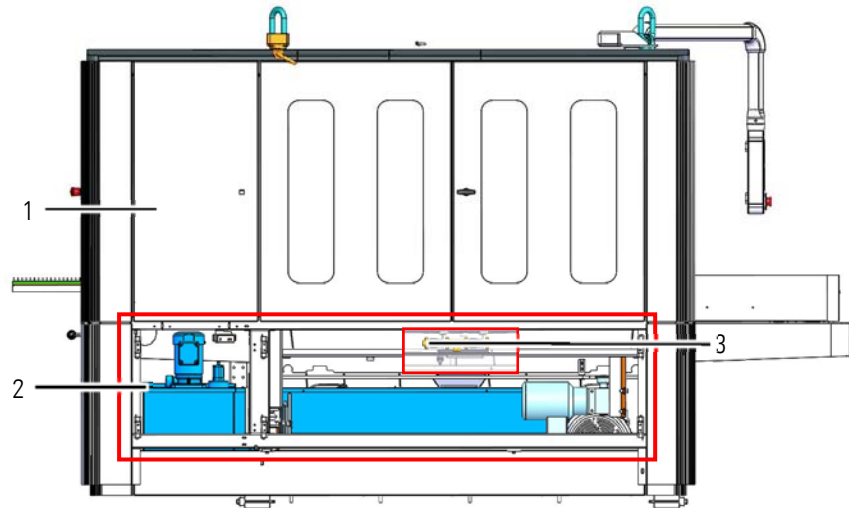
Kühlschmiermitteltank (blau, Seitenansicht)
